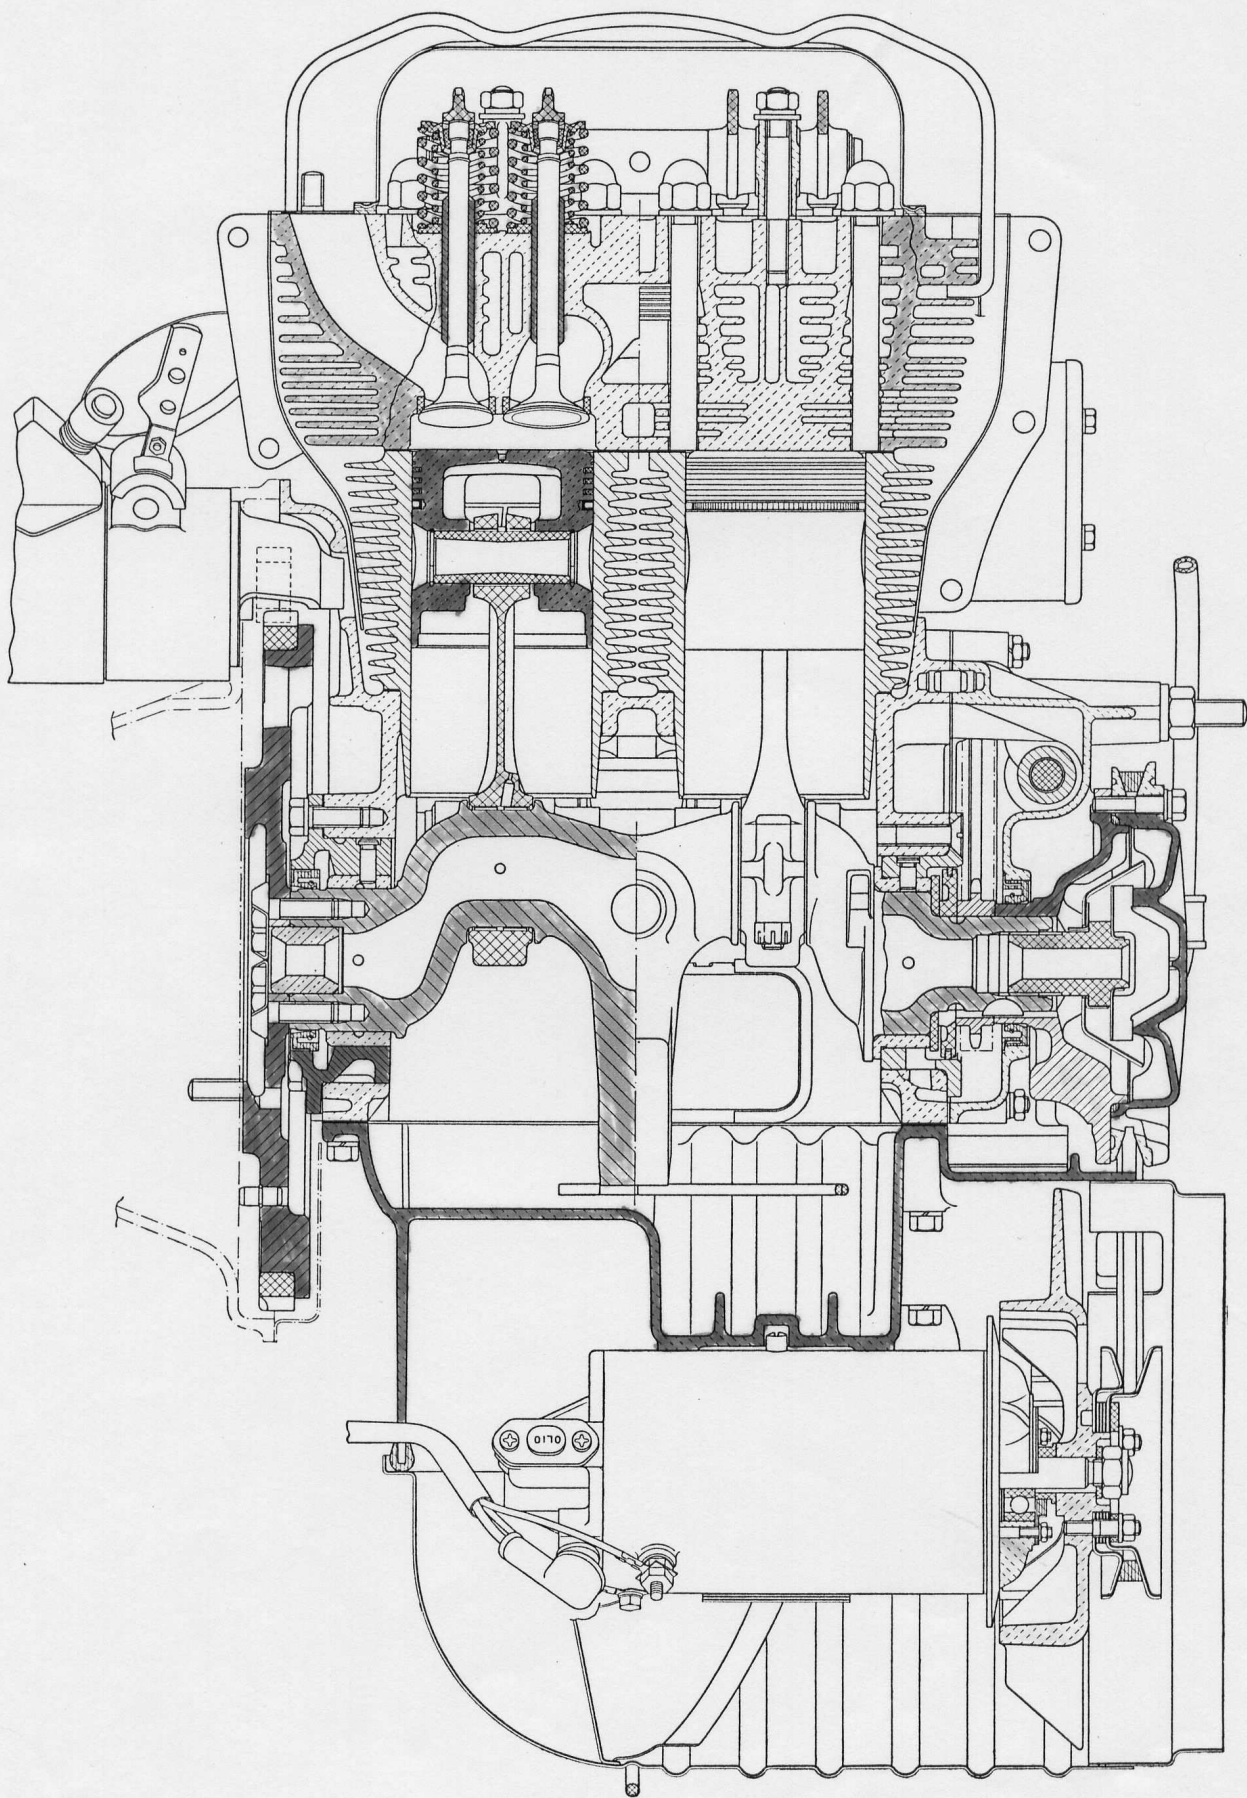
Schnitt durch die Zylinder und die Kurbelwelle.
